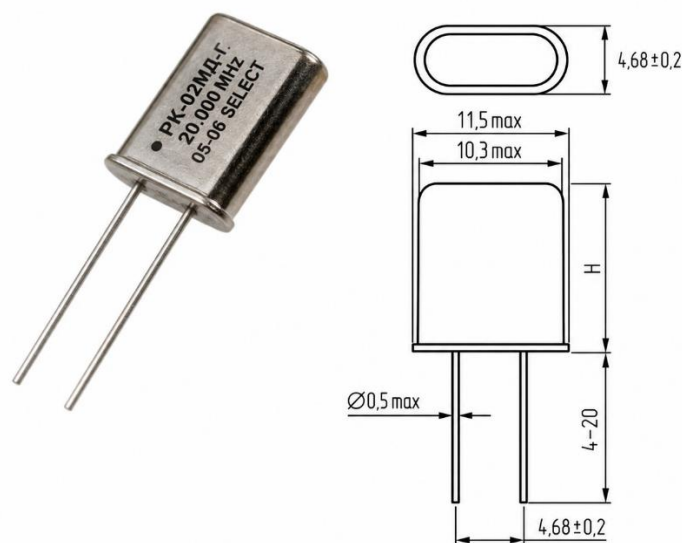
Габаритні розміри кварцового резонатора РК-02МД-Г
